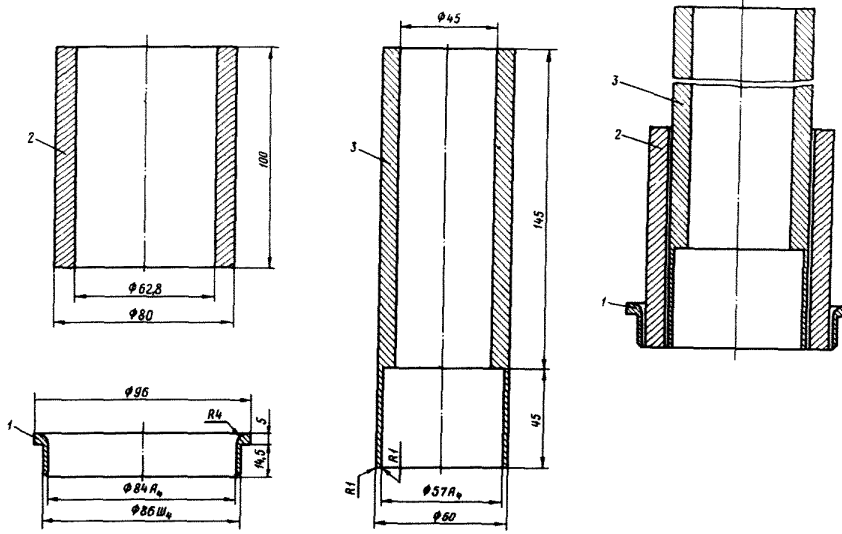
Приспособление для сборки скользящих контактов отделителя:
